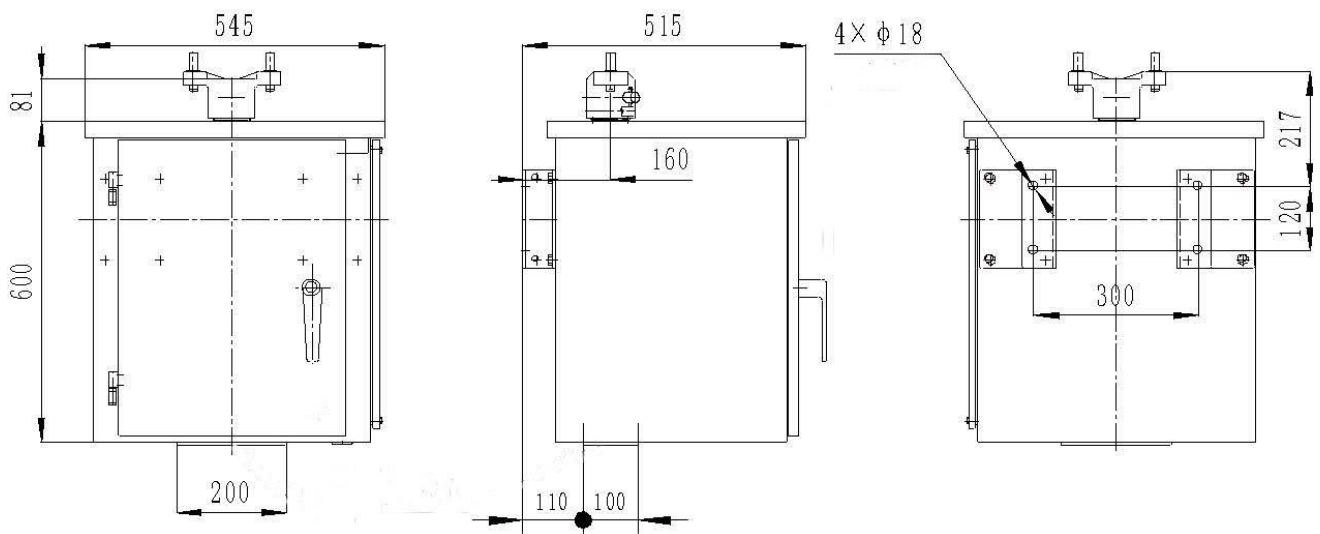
Внешний вид и габаритно-установочные размеры моторного привода ножей РГП
